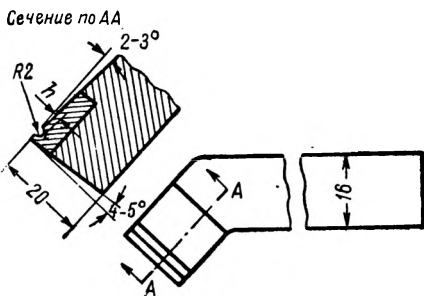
Отогнутый резец новатора П. Б. Быкова для чистовой обработки.
